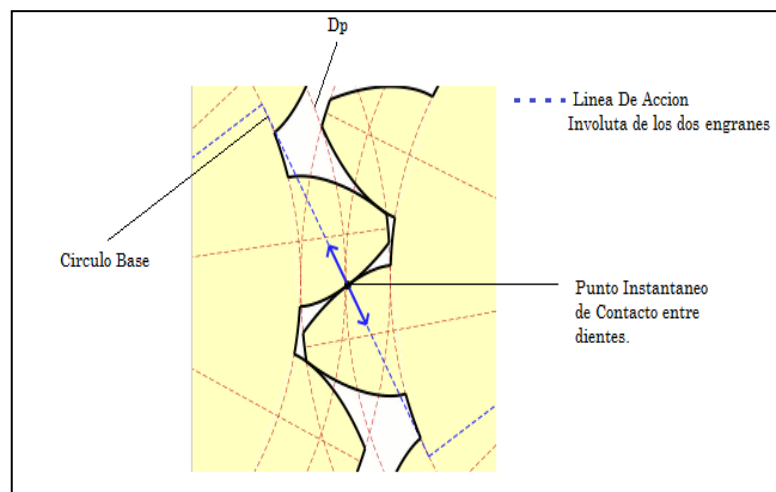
Involuta de dos Engranajes y Punto Instantáneo de Contacto⁵³
